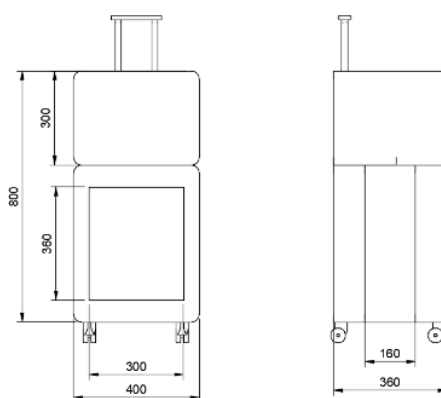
Схема комбинации модулей для четвертой группы (универсальный размер багажа)
